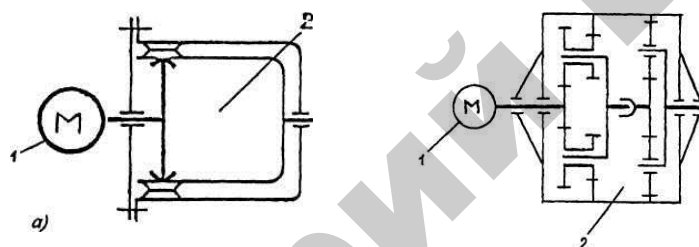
Кинематическая схема измельчителя-смесителя типа НС-80: 1 — электродвигатель; 2 — волновой мотор-редуктор
